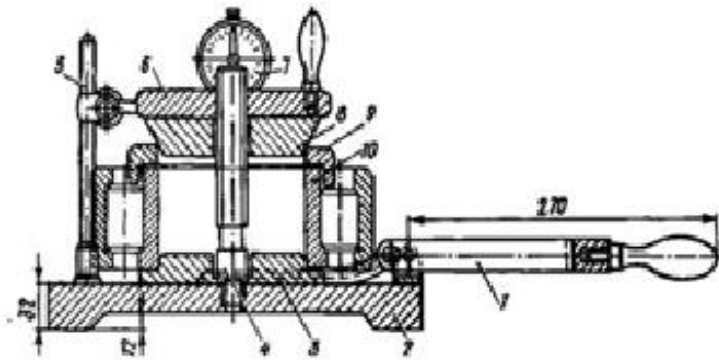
Приспособление для измерения осевого зазора между торцами роликов и бортами наружного кольца. 1 — рычаг; 2 — плита; 3 — основание; 4 — стойка; 5 — стойка штатива; 6 — гайка; 7 — индикатор; 8 — направляющий конус; 9 — прижимное кольцо; 10 — внутреннее кольцо измеряемого подшипника
